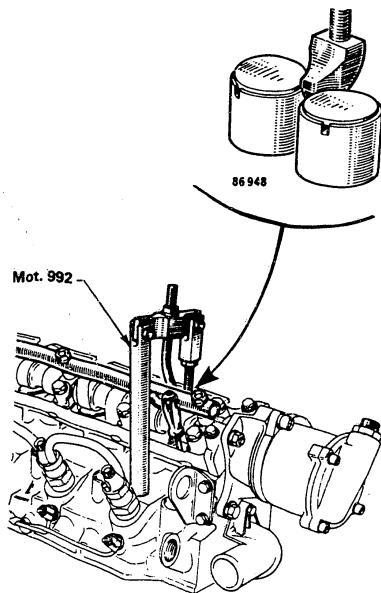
Ventilspieleinstellung mit Spezialwerkzeug Mot. 992. Das Bild zeigt den Zylinderkopf des Dieselmotors.
